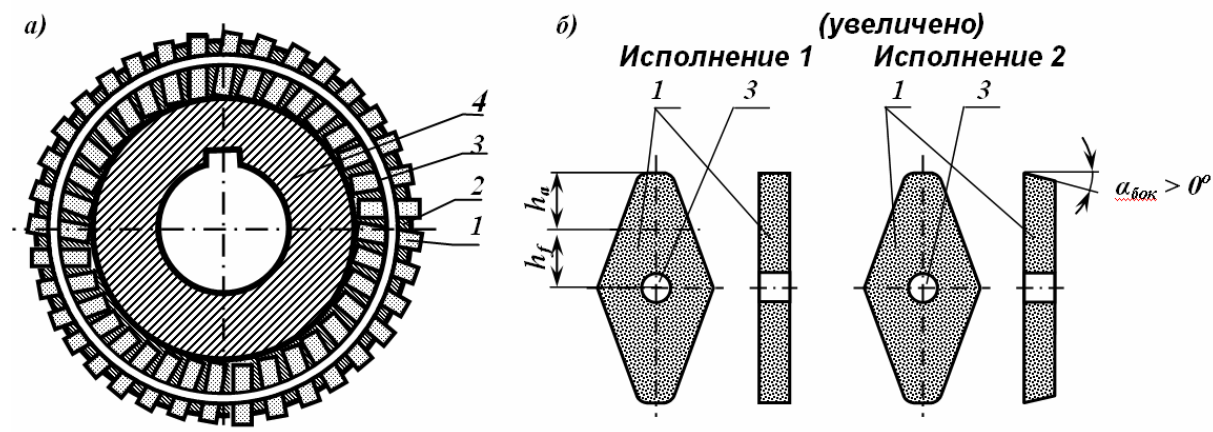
Сборная червячная фреза с установленными между витками ее корпуса неперетачиваемыми режущими пластинами, закрепленными пружинами, введенными в их отверстия (а), и режущие пластины для ее оснащения(б)
